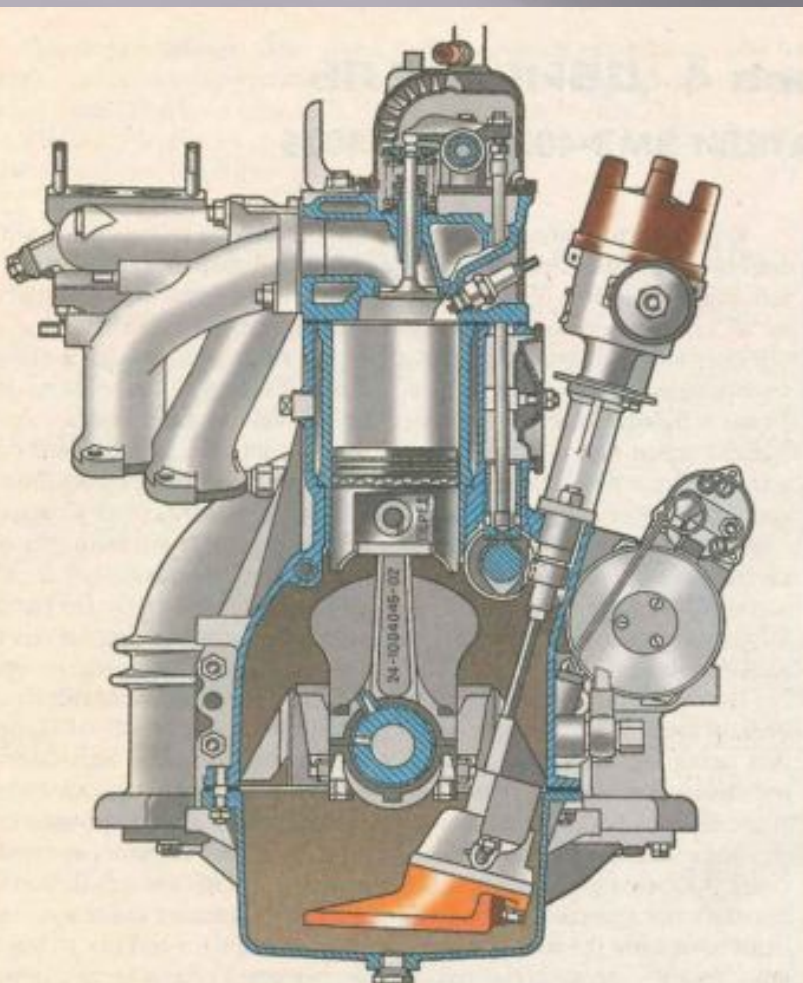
Поперечный разрез двигателя ЗМЗ 4025 (4026)
